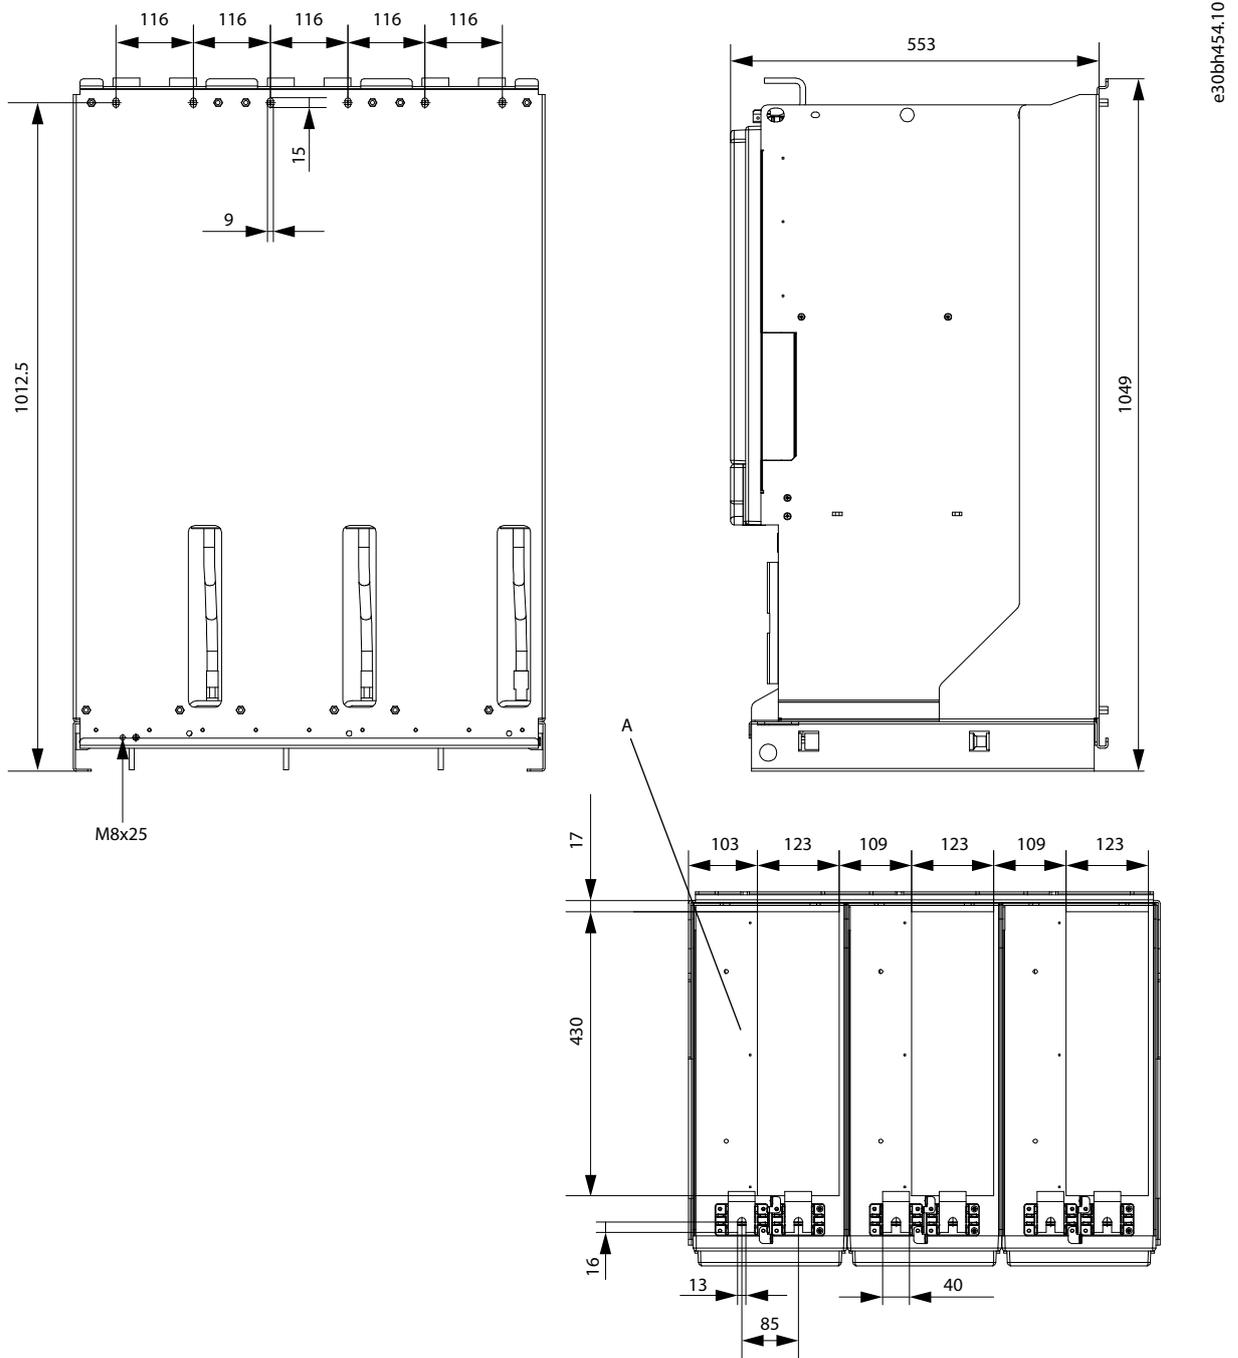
Dimensions du VACON® NX Inverter FI13, vue arrière
